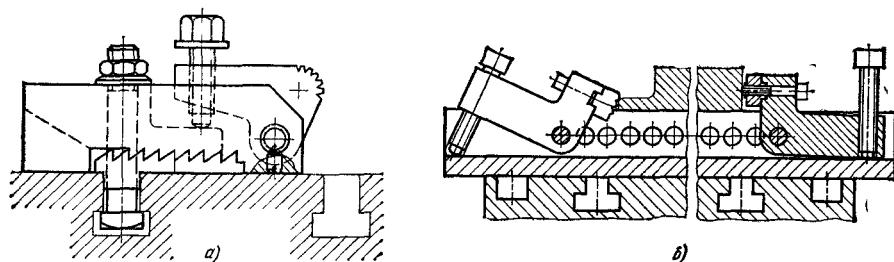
Быстроизменяемые ЗМ для закрепления заготовок сбоку с перестановкой прихватов:
